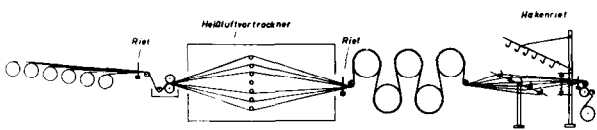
Schlichten mit kombinierter Trocknung mittels Heißluft-Trockenzylinder
